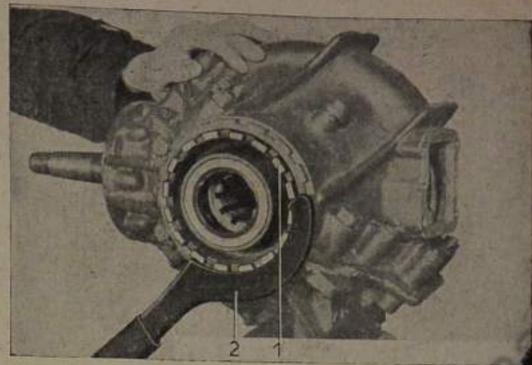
Entgegengesetzte Einstellbuchse einschrauben
